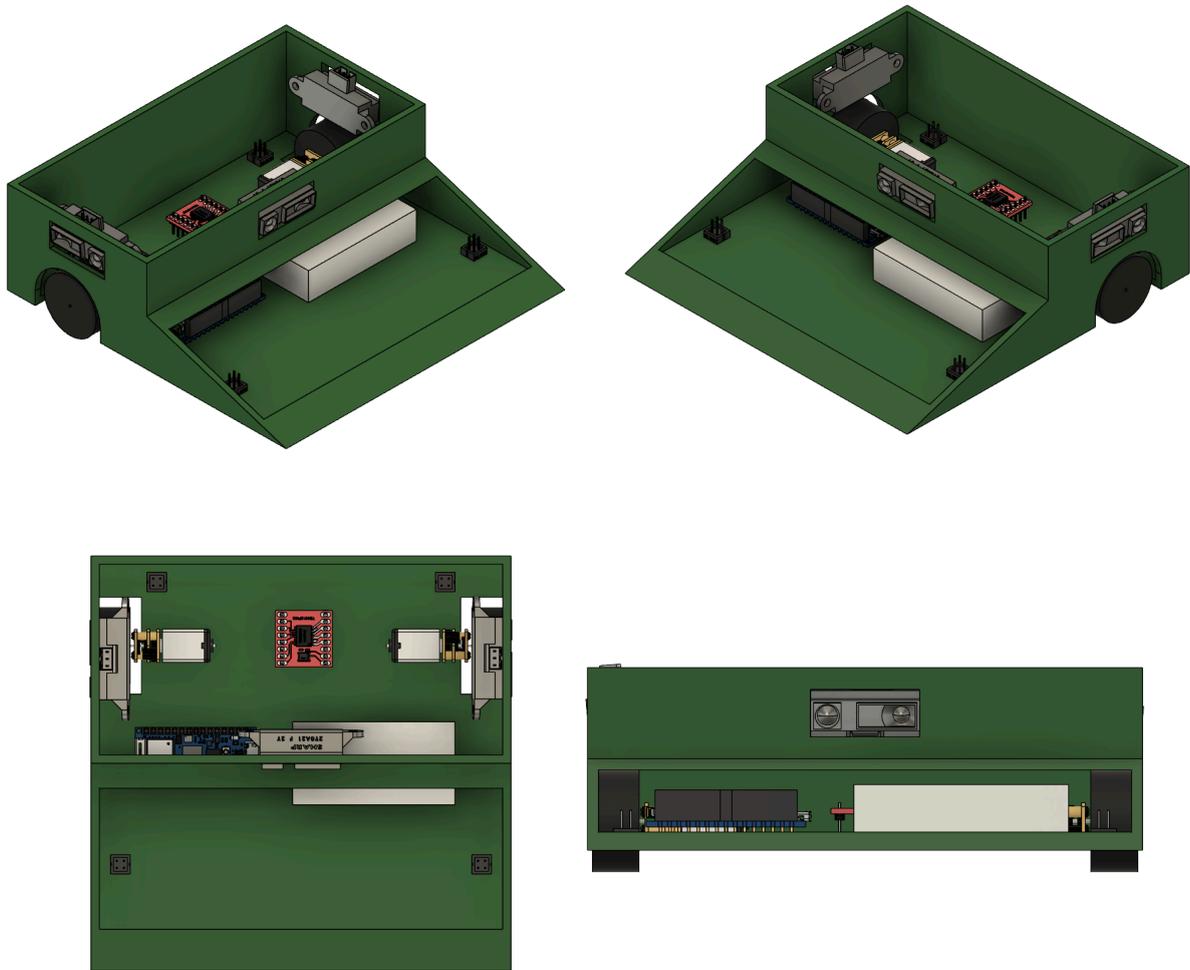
Diferentes vistas del chasis con la posición de los componentes en su interior
